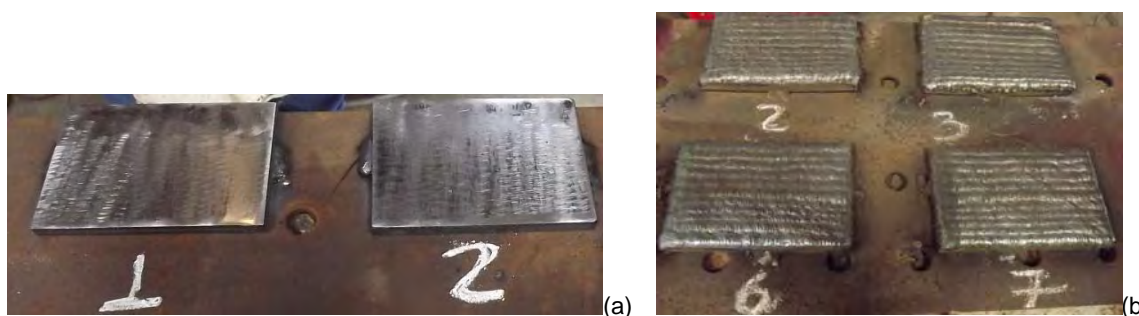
Corpos de Prova durante o processo de soldagem (a) somente lixadas antes da soldagem, (b) após a conclusão da soldagem com Cavitalloy.
